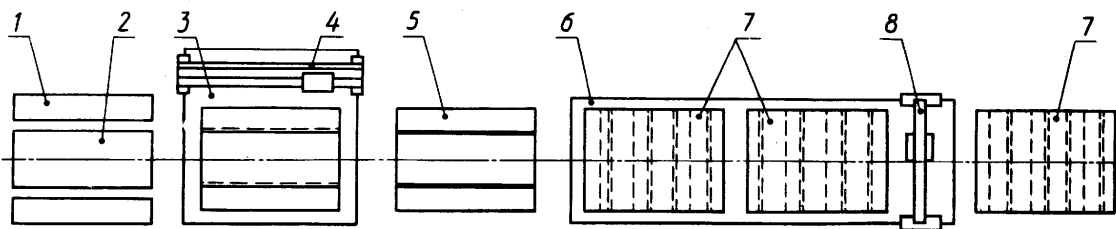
Схема поточной линии сборки и сварки секций крыши электровагона
